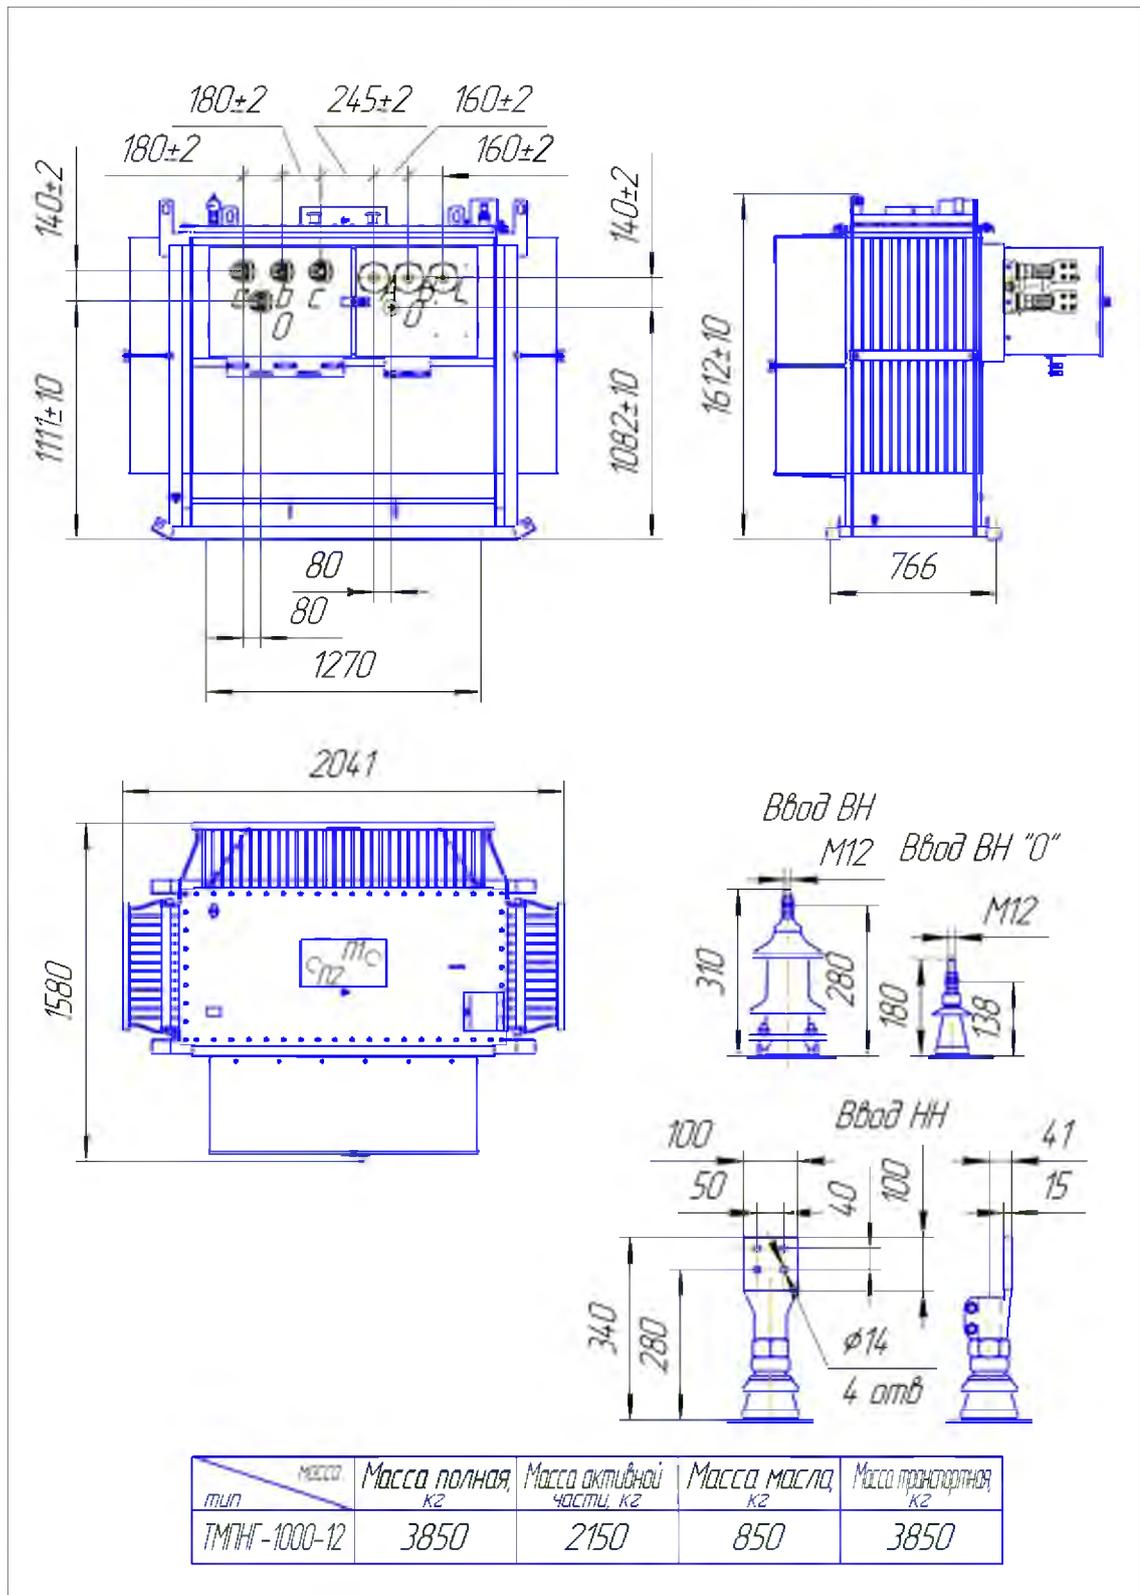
Габаритные, установочные и присоединительные размеры трансформаторов ТМПИГ-(Ч)-СЭЦ-1000/6-12
